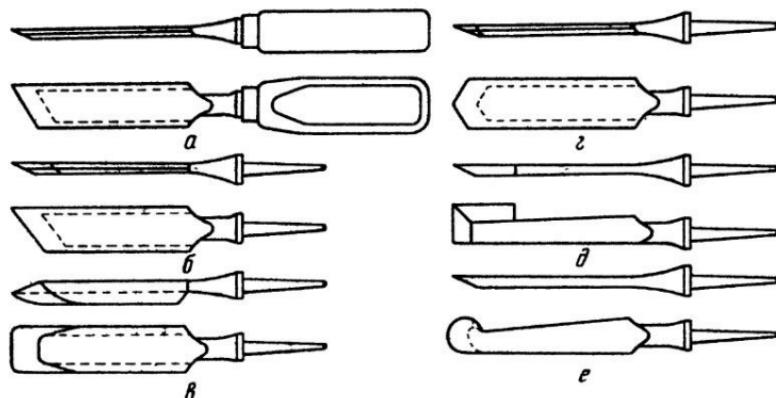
Ручные токарные резцы для обработки древесины: а — с косым расположением лезвия (косяк); б — с косым расположением лезвия (резец); в — желобчатой формы для черновой обточки; г — двухугловый; д — для прямоугольной выточки; е — для за кругленной выточки.
